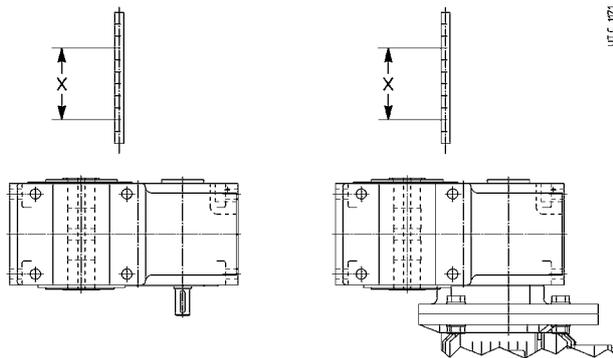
Stirradgetriebe oder -getriebemotor in Bauform V6 zur Messung des Ölstands positionieren.
